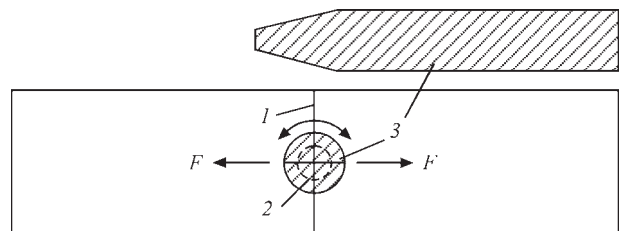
Схема ініціації руйнування зварного з'єднання з використанням отвору та циліндричного стрижня: 1 – лінія сплавлення зварного шва; 2 – наскрізний отвір у зразку; 3 – циліндричний стрижень
